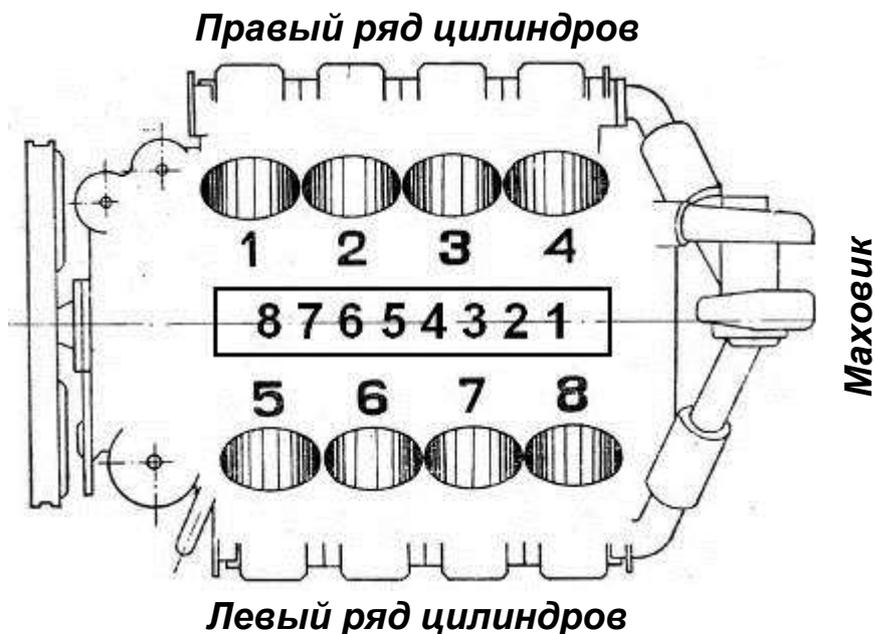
Схема нумерации цилиндров двигателя и секций ТНВД
